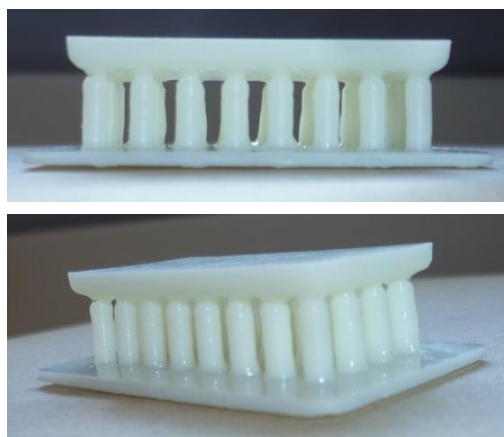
Pieza probeta 1. Arriba, vista frontal. Abajo, vista isométrica.
